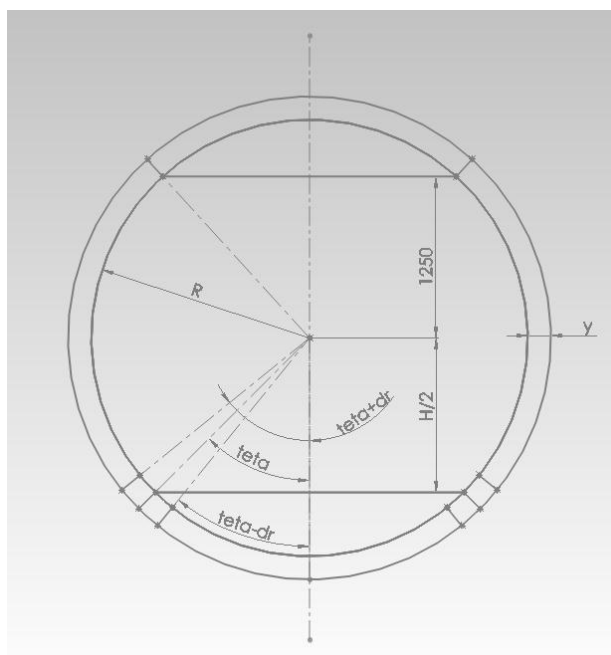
Secção frontal do modelo de construção da estrutura tubular (mm).
